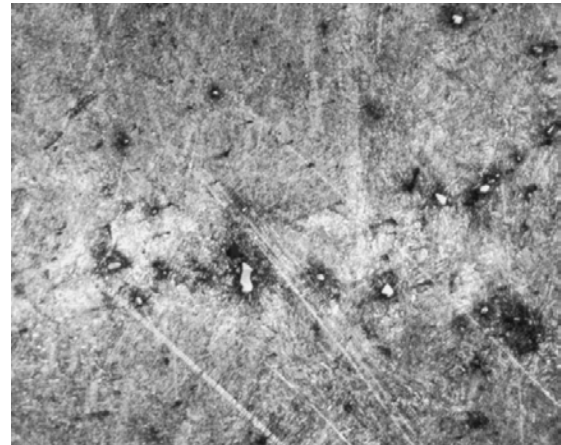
Дефекты литой заготовки из стали 35Л в зоне сварного шва
